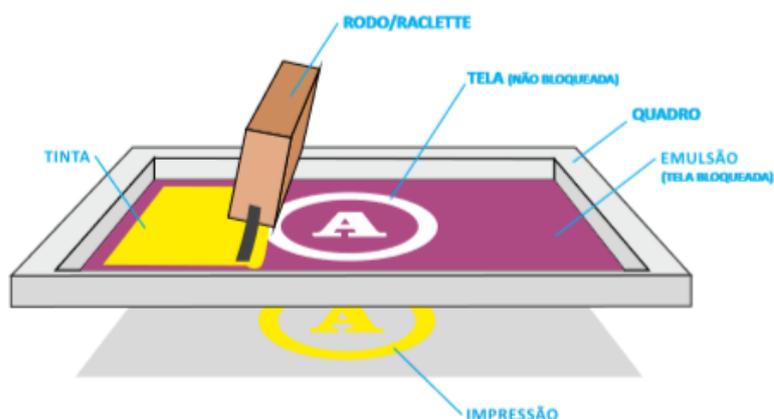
Princípio de Impressão da Estamperia (Paul Stricker, 2021).
